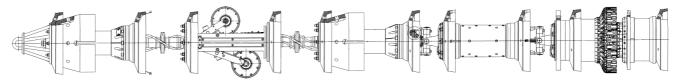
Чертеж общего вида дефектоскопа внутритрубного магнитного 8-MCK.01-00.000 и 8-MCK.01-00.000-01
